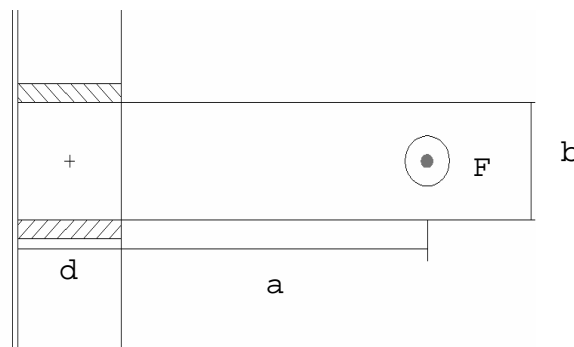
b.- DCL Soportes soldados de la mesa
